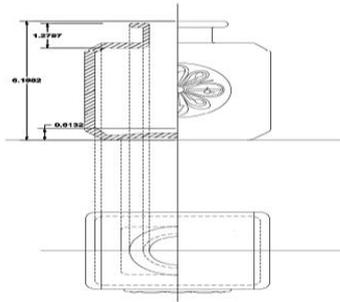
مسقط رأسي وأفقى وقطاع للفكرة التصميمية الأولى
